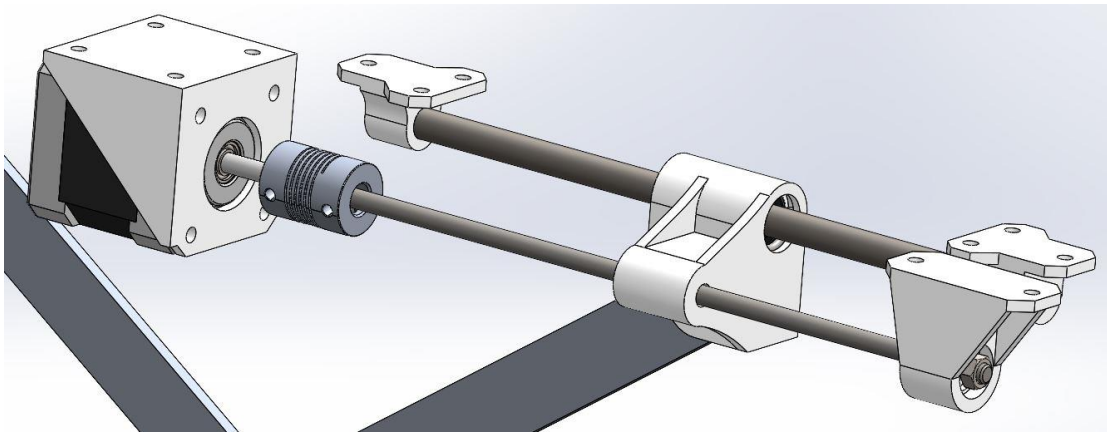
Soporte del motor (izquierda), y soporte para los rodamientos axiales (derecha).
